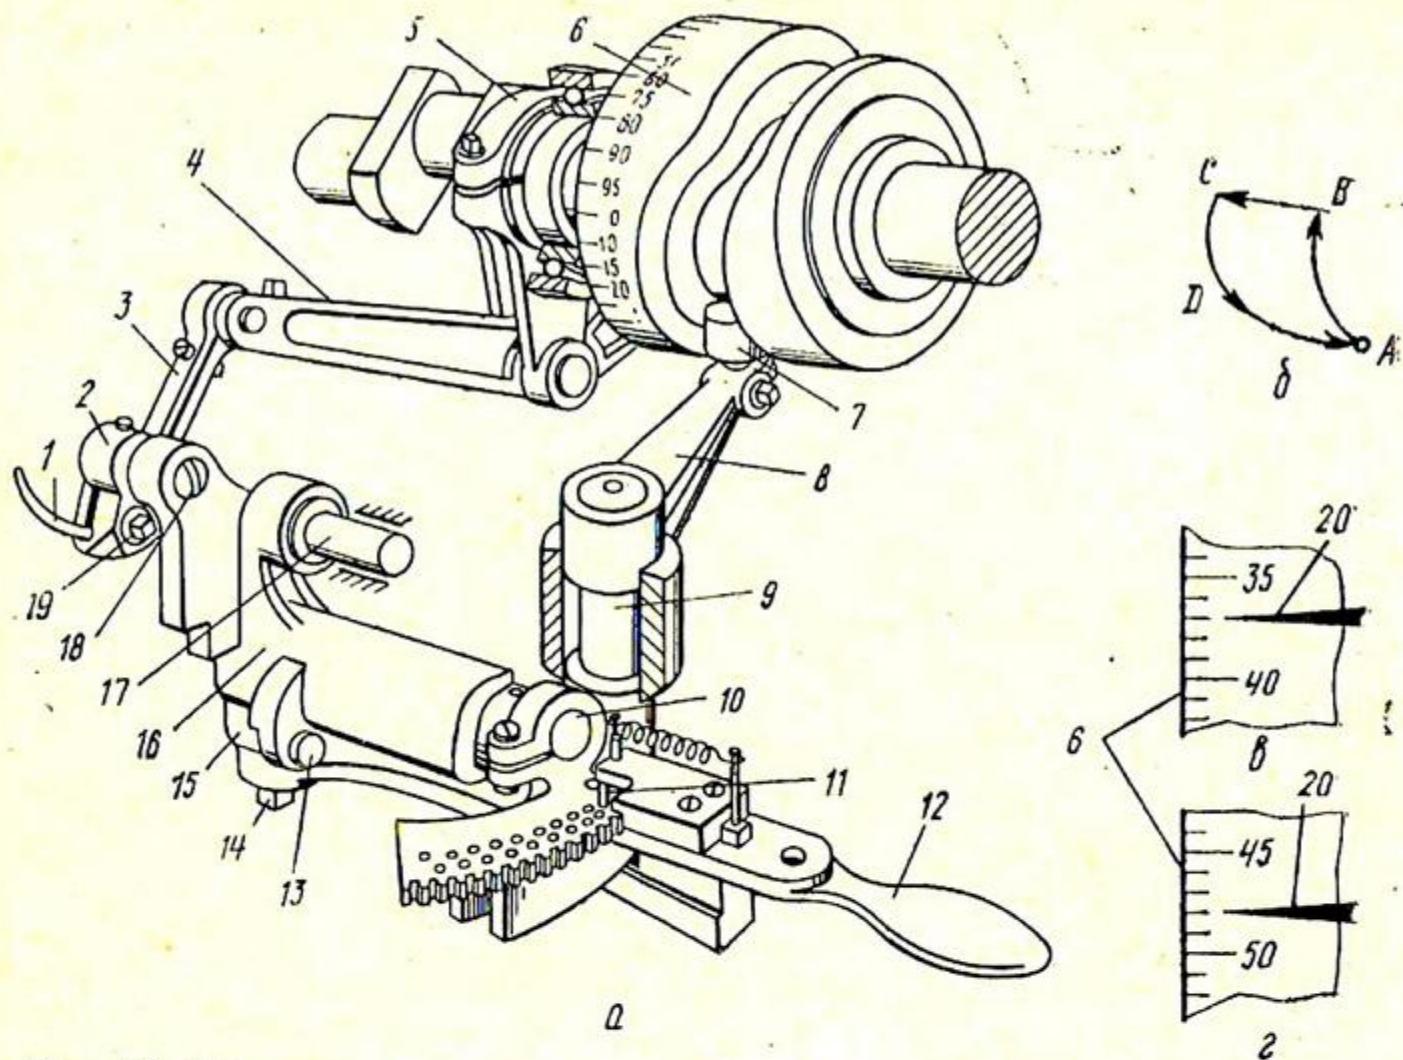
Механизм шила машины СПР (а), траектория движения шила (б), положения главного вала при установке (в) и регулировке (г) шила
